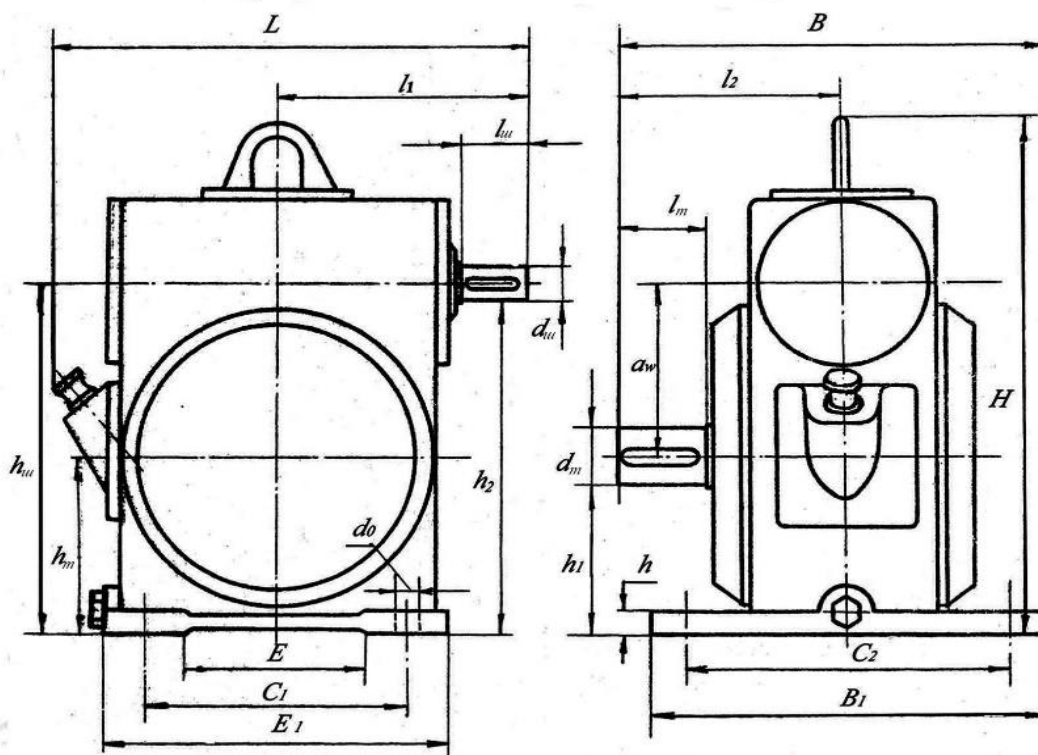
Розмірна схема черв'ячного редуктора
